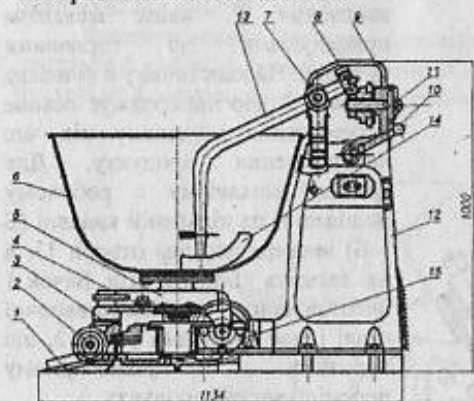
Тістомісильна машина ТММ-1М: 1 – фундаментна плита; 2, 15 – поворотні колеса; 3 – пересувний візок; 4 – диск; 5 – кожух; 6 – діжа; 7 – шариковий підшипник; 8 – кривошип; 9 – нерухлива вісь; 10 – рукоятка; 11 – зірочка; 12 – станина; 13 – місильний важіль; 14 – лопать
